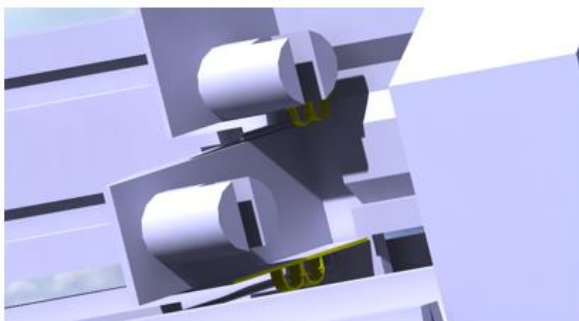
Assurer la torsion des circuits doubles au niveau des machines Komax BT288.
